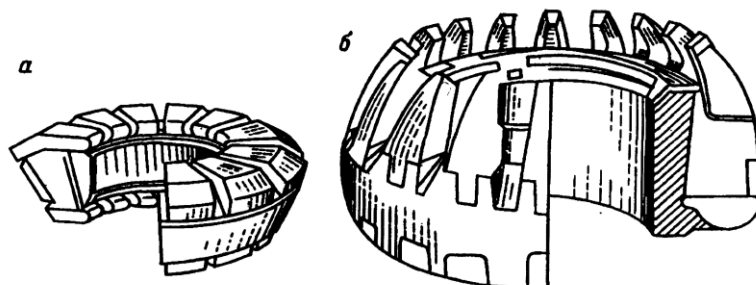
Уплотнители ПУ: а – типа ПУ1; б – типа ПУ2
